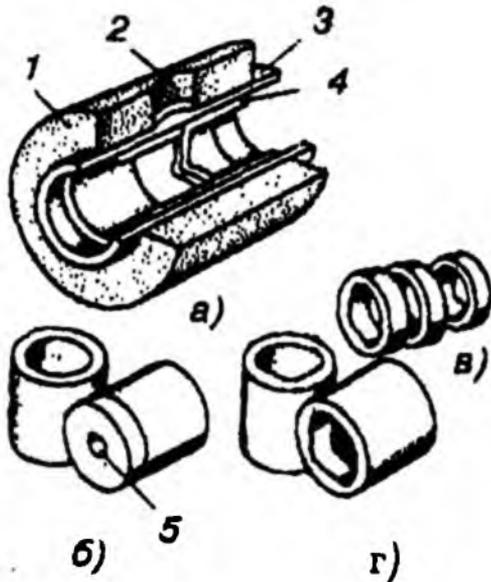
Патрон ПА для термитной сварки:
